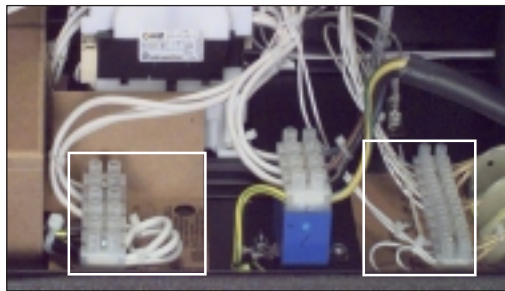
Klemmbrett für Schweiß- und Steuertrafo
